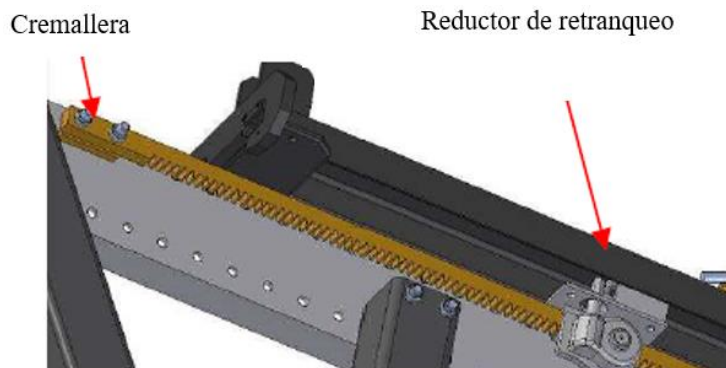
Detalle del sistema de retranqueo. Recuperado de: Ulma Construction, *Consolas autotrepantes*.
